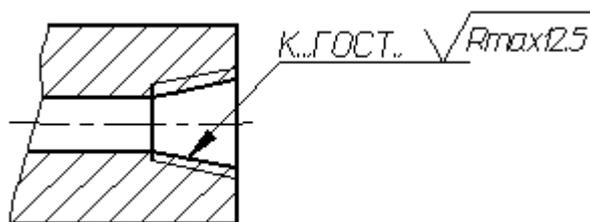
Пример обозначения шероховатости внутренней конической резьбы
